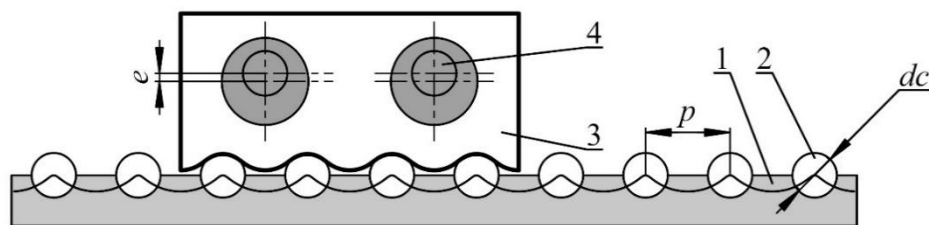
Схема линейной планетарно-цевочной передачи. 1 – рейка; 2 – цевка; 3 – сателлит; 4 – эксцентрик.
